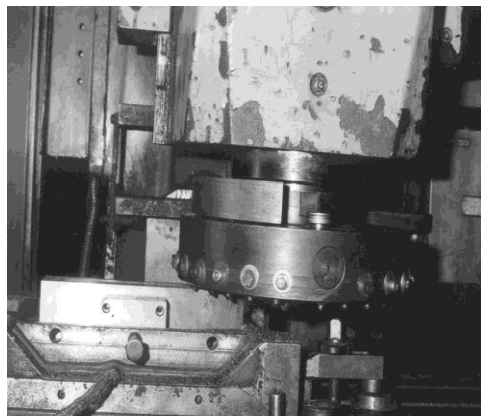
Схема взаємного розташування інструмента і заготовки
